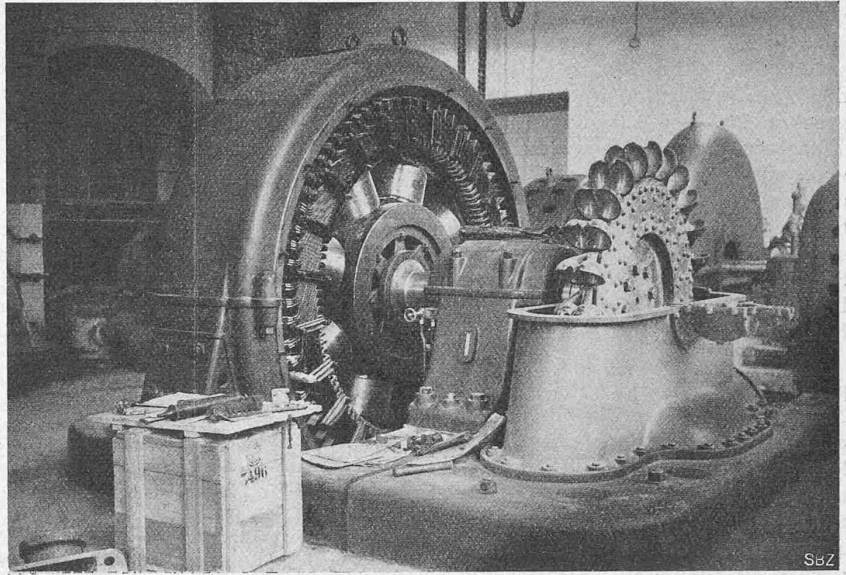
2600 KVA-Maschinengruppe während der Montage.
